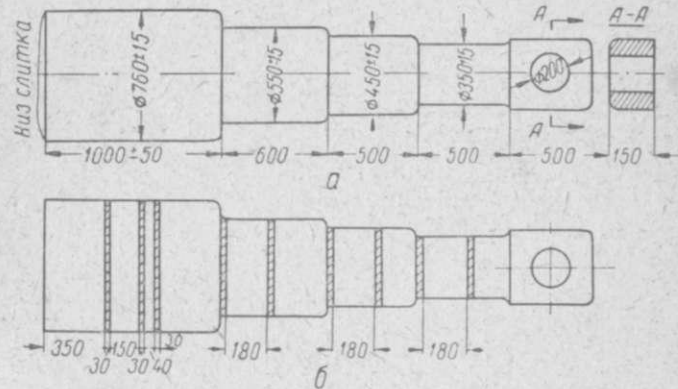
Эскиз ступенчатой поковки (а) и схема вырезки образцов (б).
